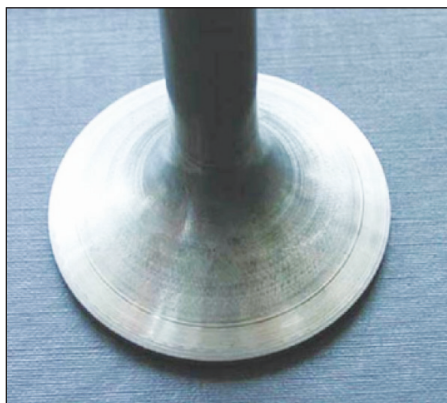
Подготовленная поверхность тарелки клапана для лазерной порошковой наплавки
